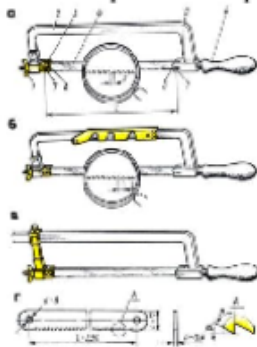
Ручная ножовка (станок): а - цельная, б - раздвижная, в - с передвижным держателем, г - ножовочное полотно; 1 - гайка-барашек, 2 - рамка (станок), 3 - подвижная головка, 4 - ножовочное полотно, 5 - неподвижная головка, 6 - хвостовик с ручкой, 7 - штифты, 8 - прорезы
